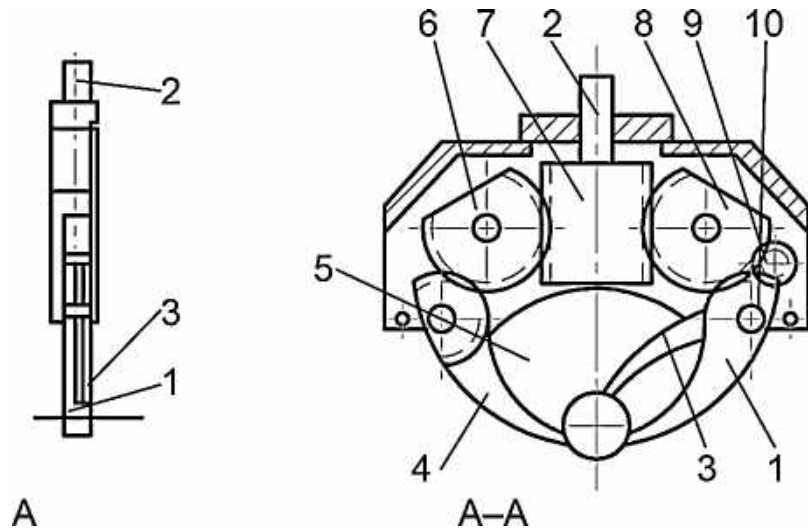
Центрувальний вузькодіапазонний двопозиційний захоплювальний пристрій послідовної дії
